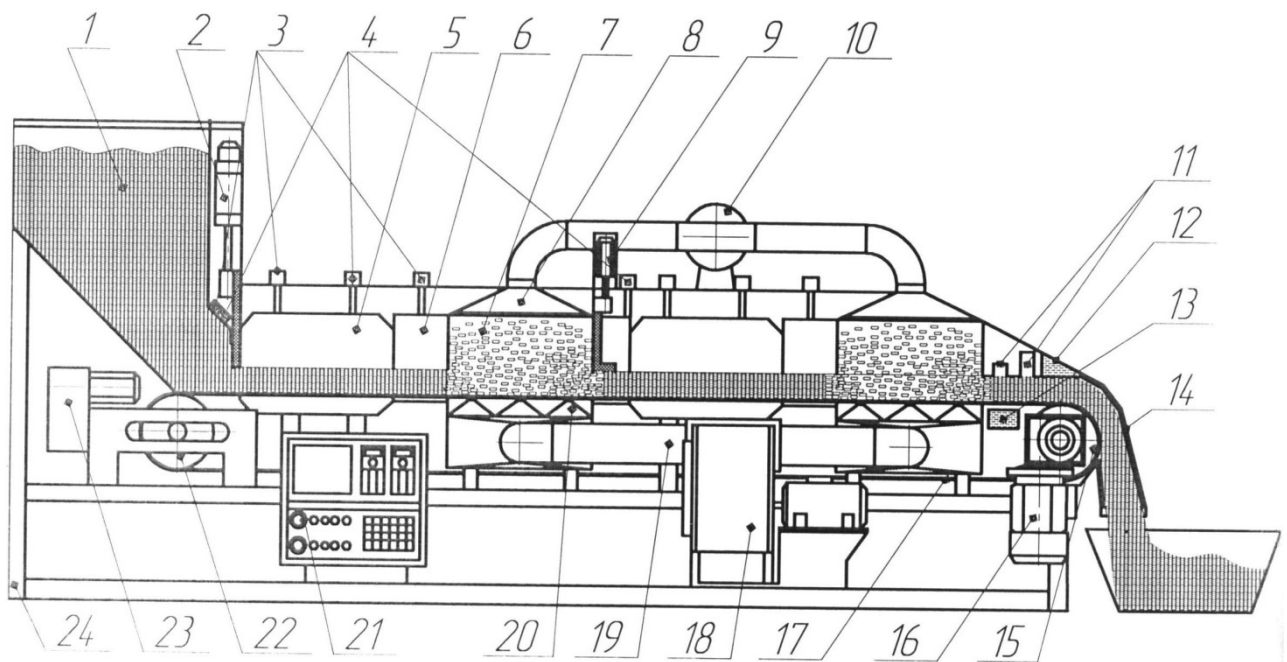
Схема установки НВЧ обробки вугілля
